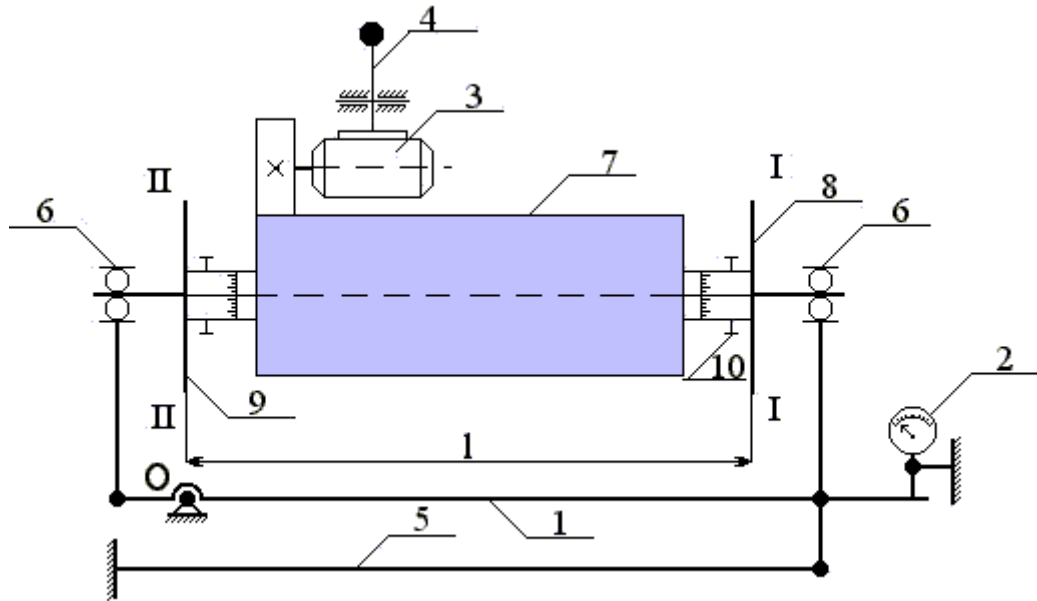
Схема станка для динамической балансировки ротора: 1 - рама; 2 - индикатор; 3 - электромотор; 4 - рукоятка; 5 - торсионная пружина; 6 - подшипник; 7 - уравниваемый ротор; 8, 9 - диски для установки уравнивающих масс; 10 - винт фиксации угловой координаты
